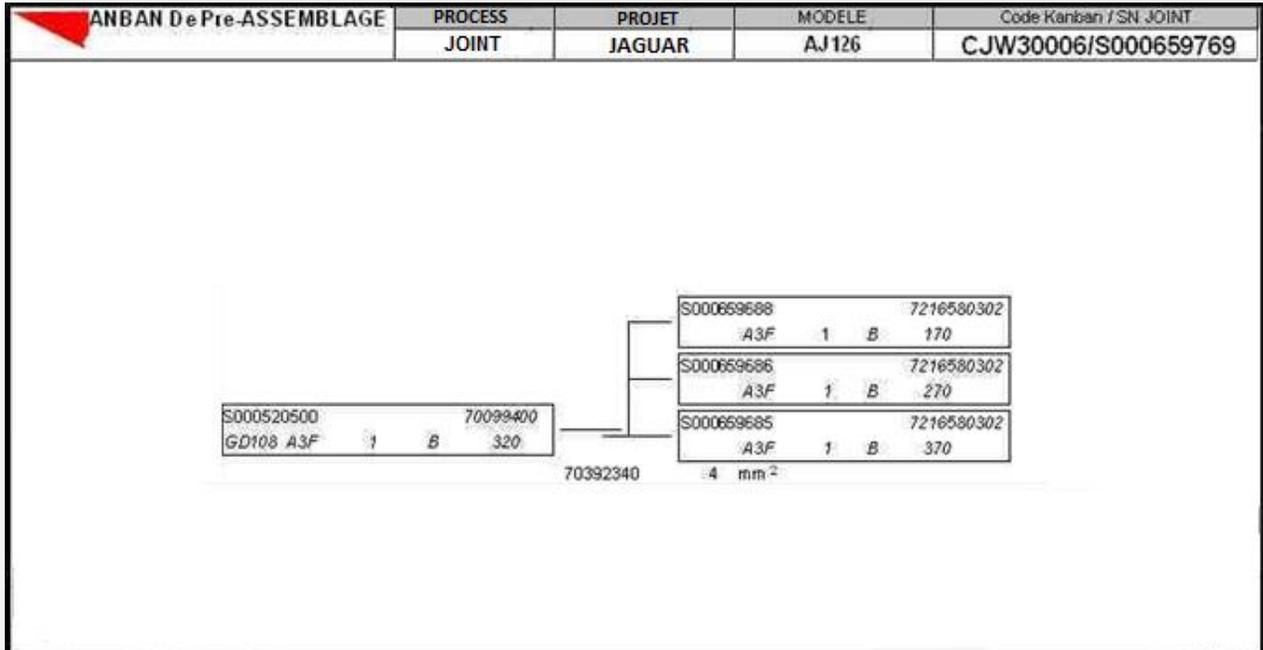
Exemple de dessin explicatif d'un joint de la famille DPLA
